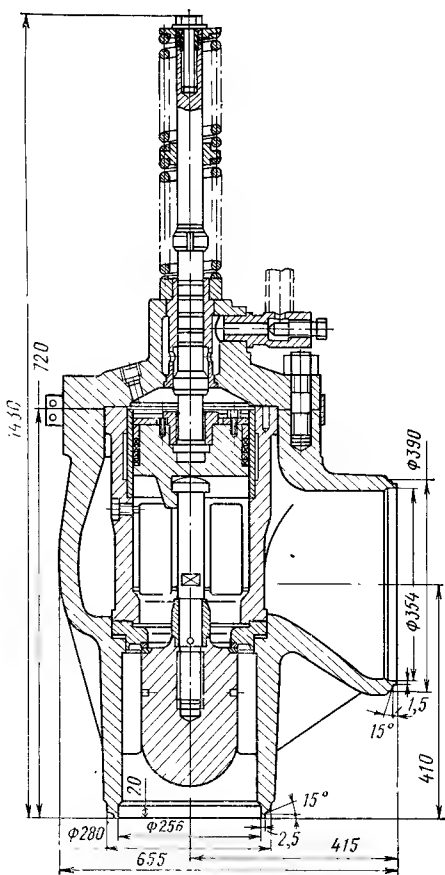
Предохранительный главный клапан Э-2875-0 на $p_p = 6$ МПа.
